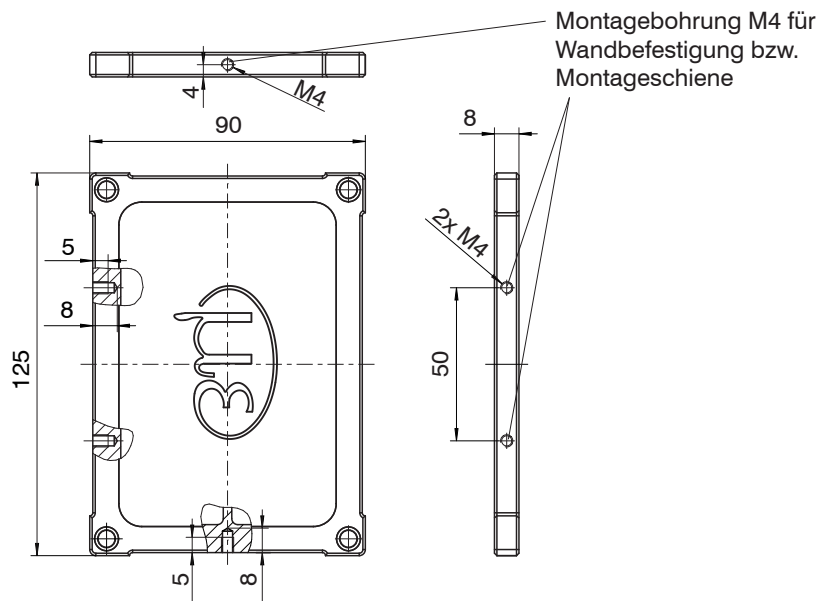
Maßzeichnung Gehäusedeckel, Abmessungen in mm
